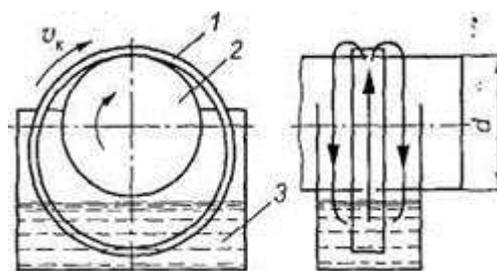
Смазывание подшипника кольцом: 1 — кольцо; 2 — цапфа; 3 — резервуар для масла
